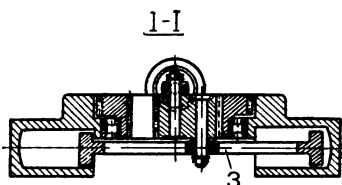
Схема двигателя (конструктор Е. И. Лев):
